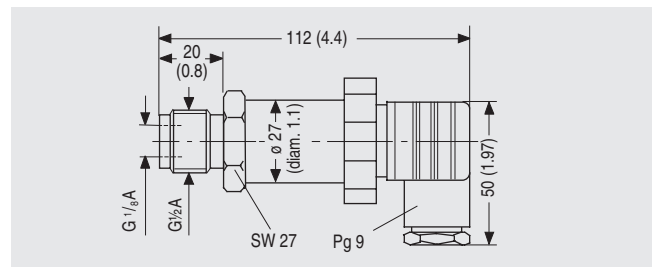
/4 Измерительный преобразователь избыточного давления 7MF1562, размеры в мм (дюймах)
